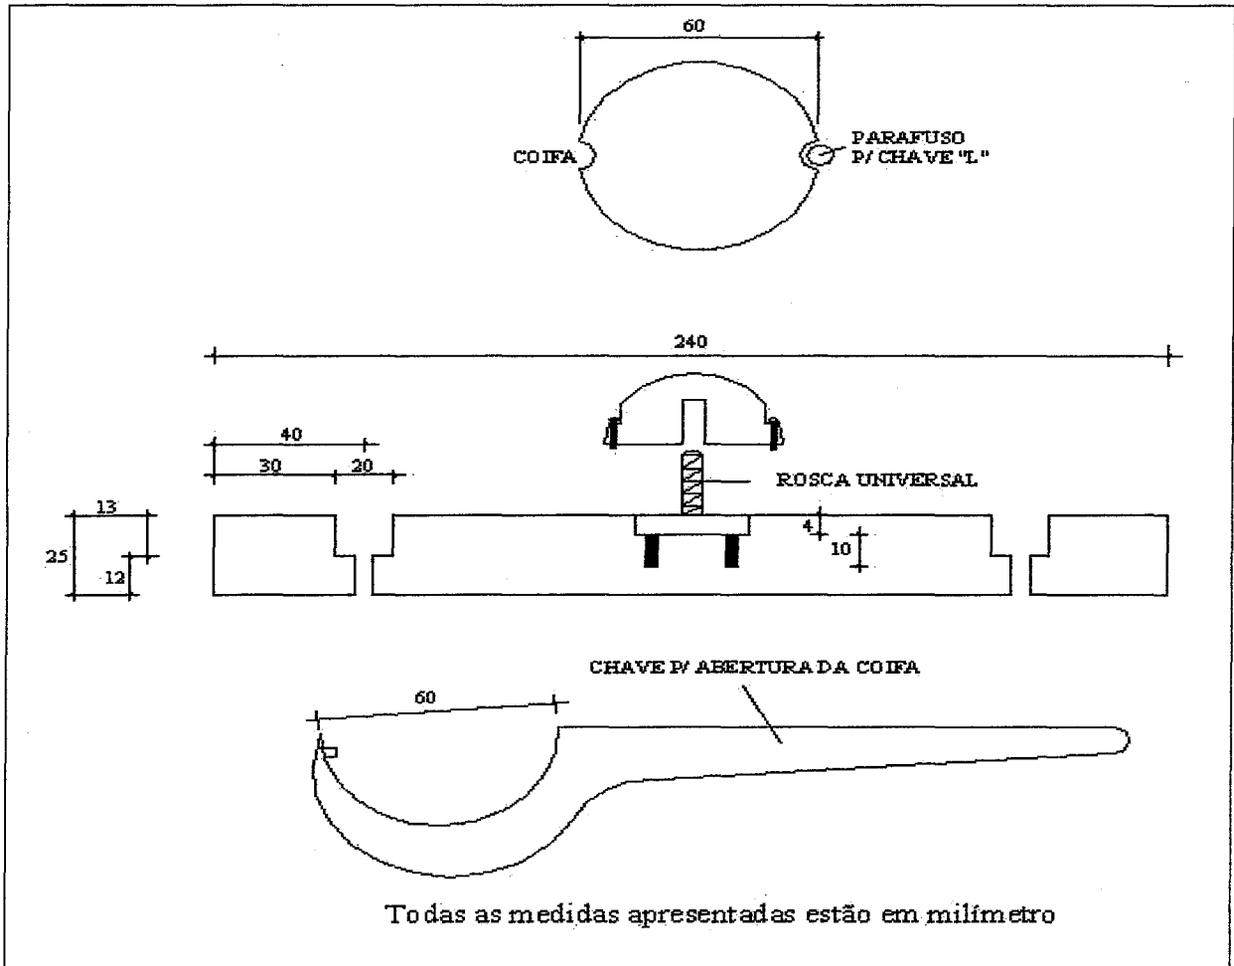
Detalhamento do dispositivo de centragem forçada e chave.
